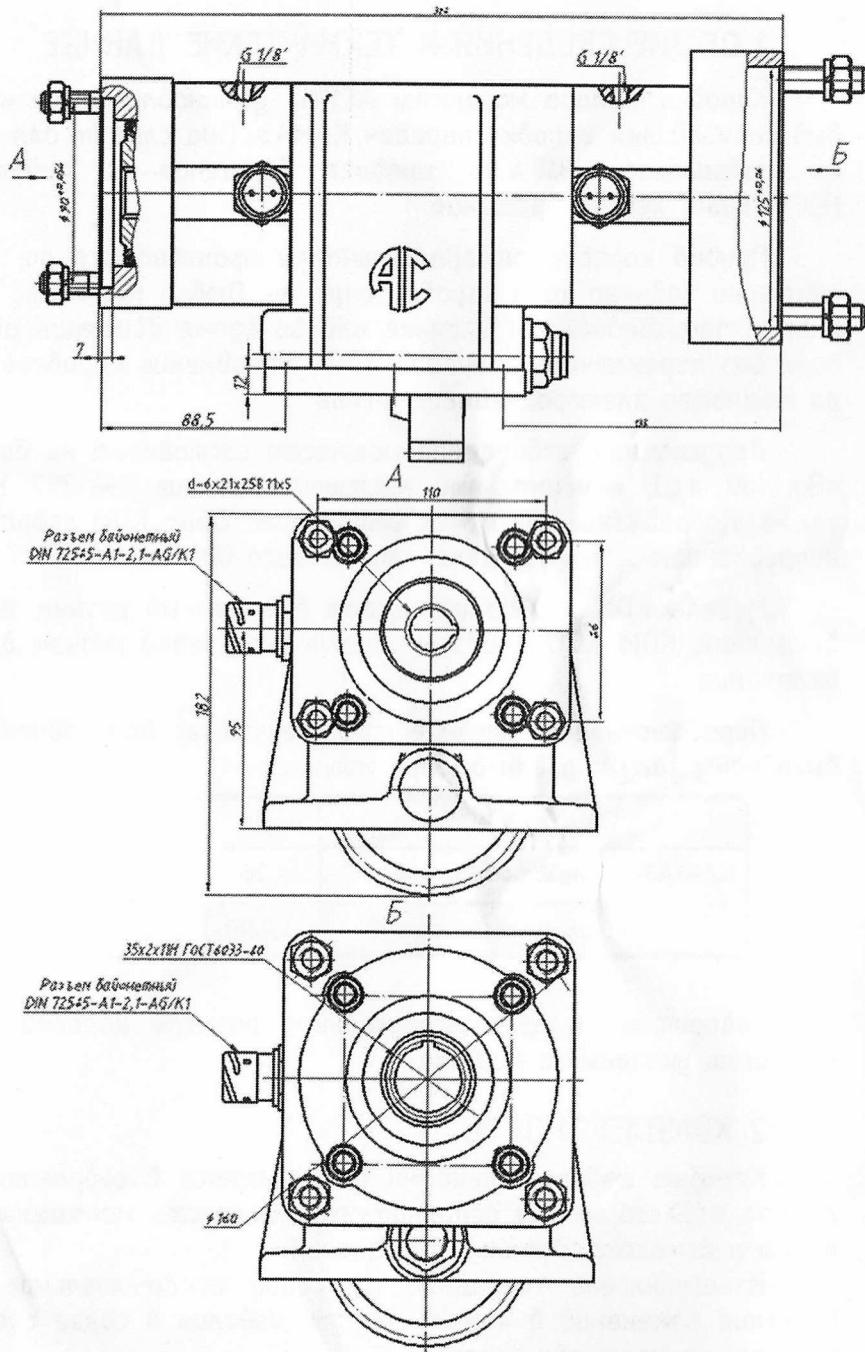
Габаритные и присоединительные размеры АС1753-010
